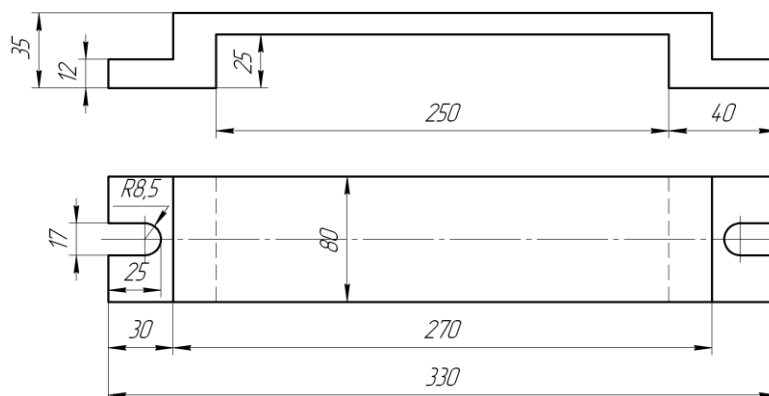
Приклад плоскої поверхні нежорсткої деталі, що підлягає обробці торцевим фрезеруванням
